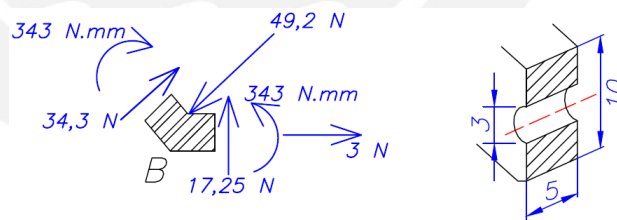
Fuerzas y dimensiones en la sección "B".
